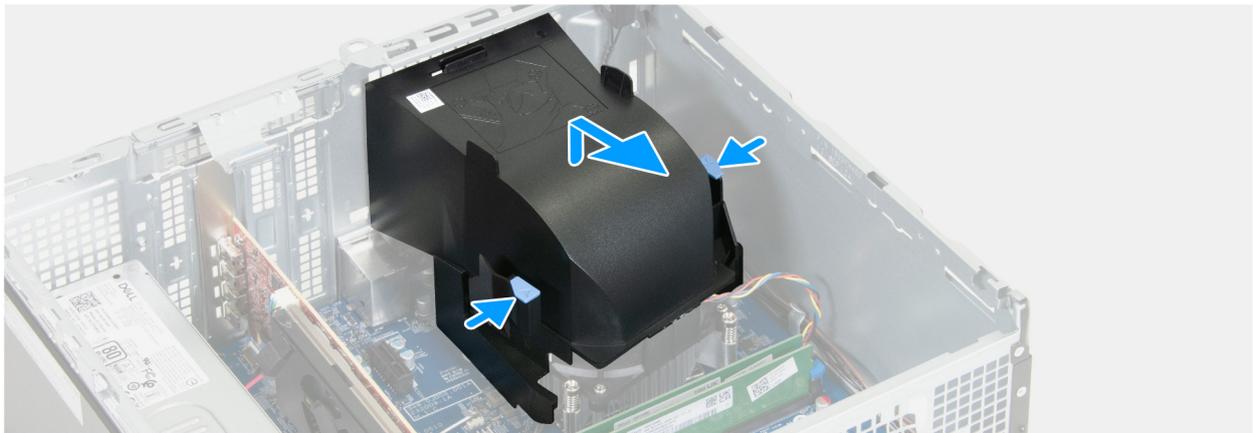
Imagen: Extracción de la cubierta del ventilador
